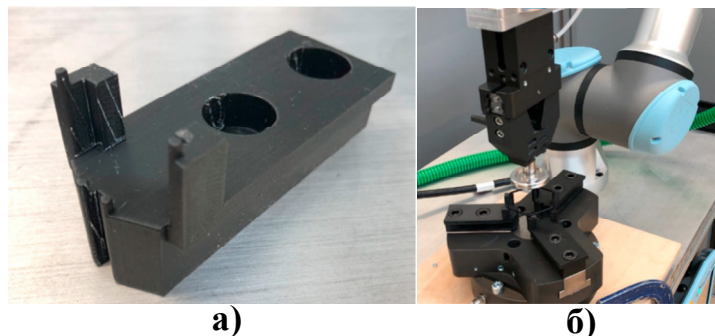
Установка уплотнительного кольца в канавку поршня: а – специальный палец для приспособления; б – уплотнительное кольцо
